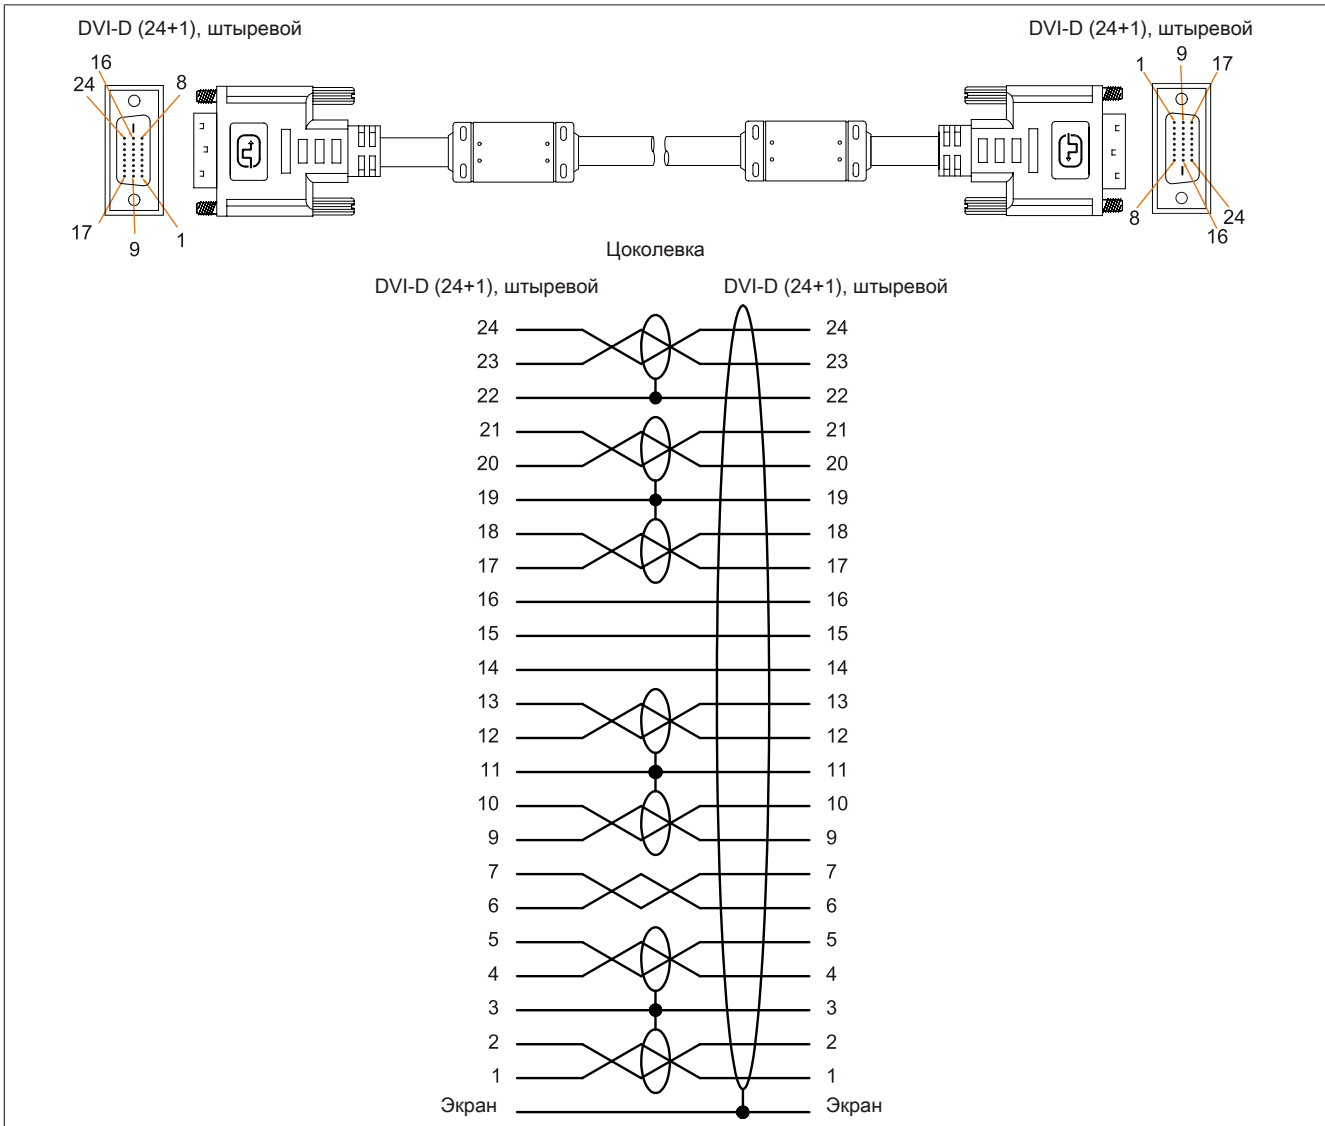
5CASDL.0xxx-00 — цоколевка
